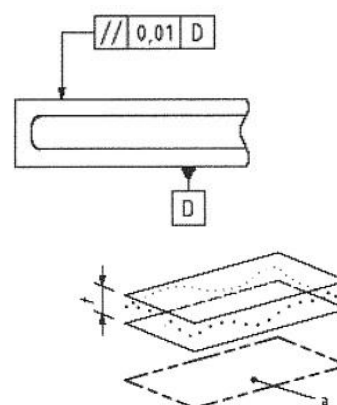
Označení a vysvětlení geometrické tolerance rovnoběžnosti přímky s rovinou [4]
